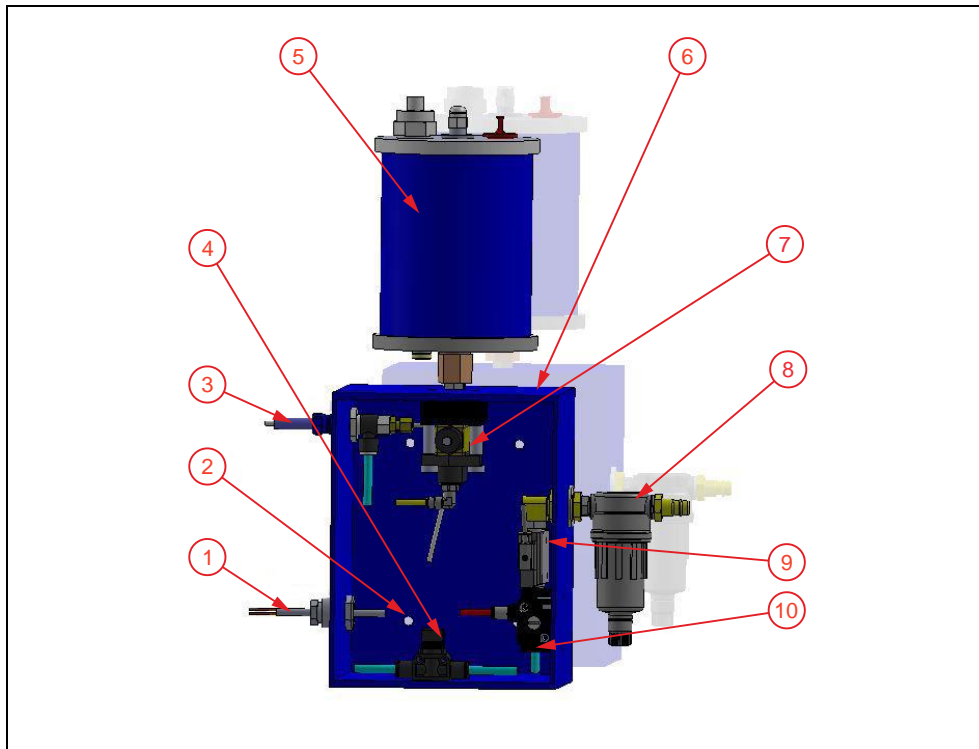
Principales componentes del aplicador equipado con bomba de bronce
